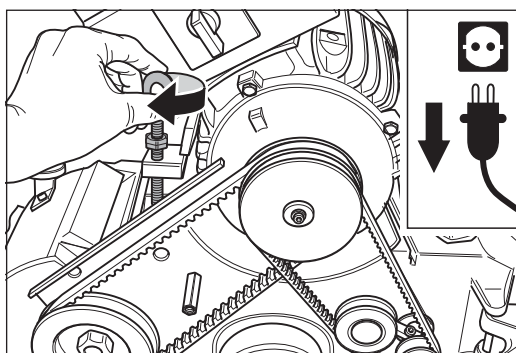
Die beiden Keilriemen auflegen und zum Spannen die Ringschraube am Motor im Uhrzeigersinn drehen.
